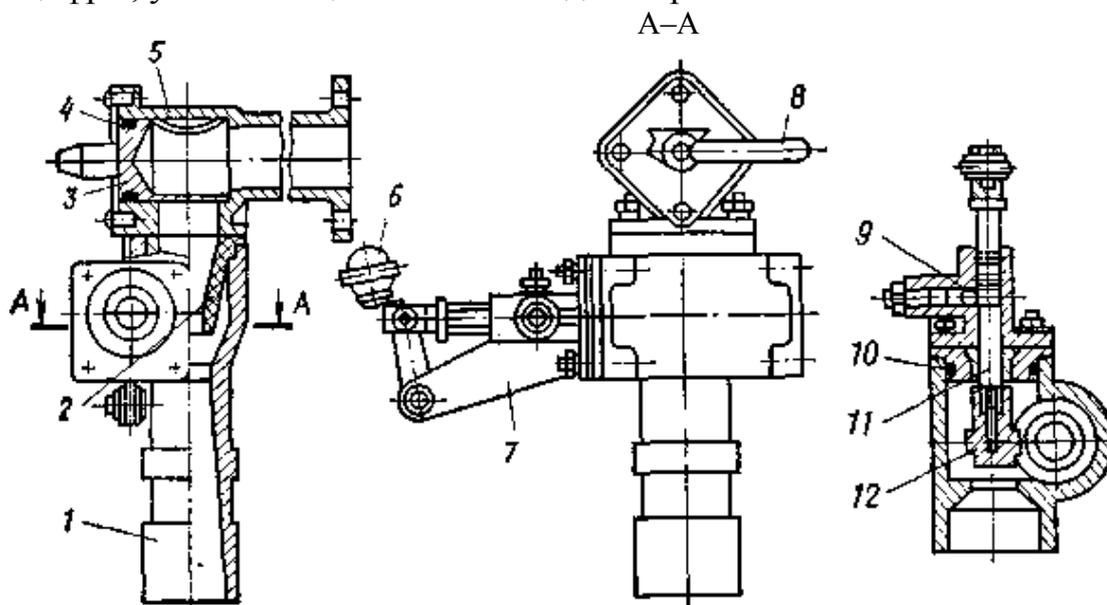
Пеносмеситель ПС–12: 1 – диффузор; 2 – сопло; 3 – пробка крана; 4, 10 – уплотнительные кольца; 5 – корпус крана; 6 – рукоятка дозатора; 7 – кронштейн; 8 – ручка крана; 9 – фиксатор; 11 – шток; 12 – пробка дозатора
